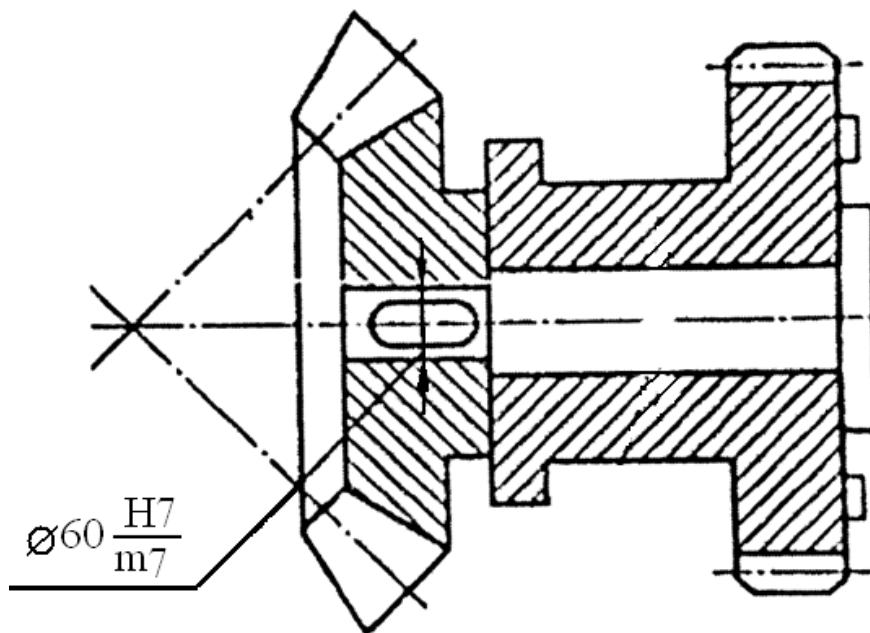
Посадка конического зубчатого колеса на вал с дополнительным креплением шпонкой
